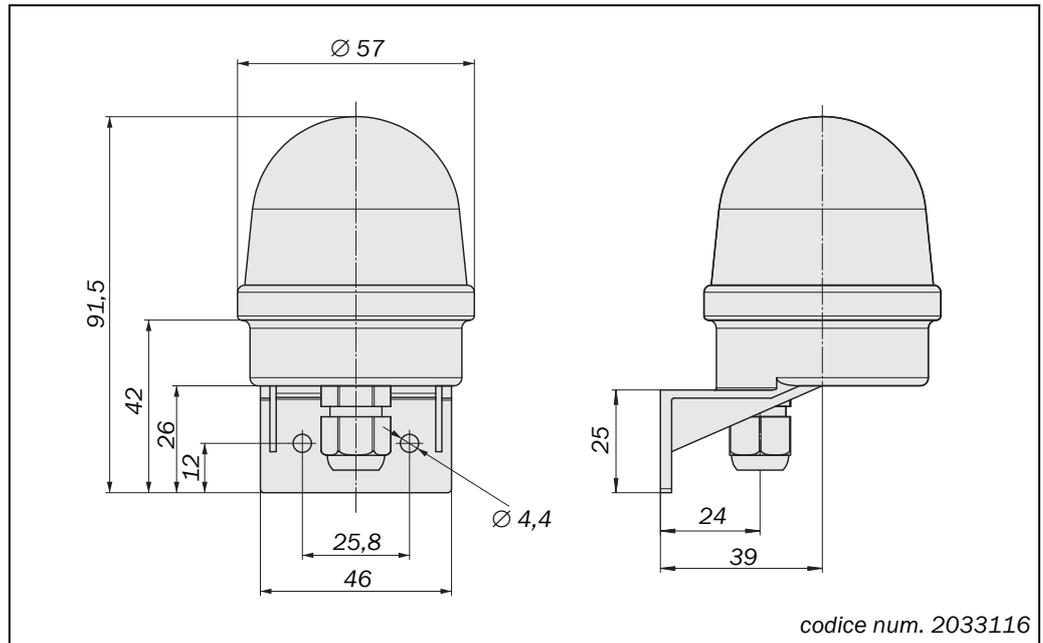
disegno quotato del dispositivo di comando UE403 (mm)
